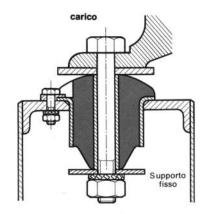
Montaggio ai piedi della macchina e chassis metallico
